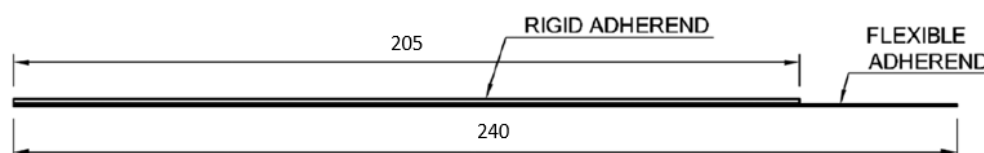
Configuração da geometria dos provetes *floating roller peel test*. (Adaptado de [77]).
